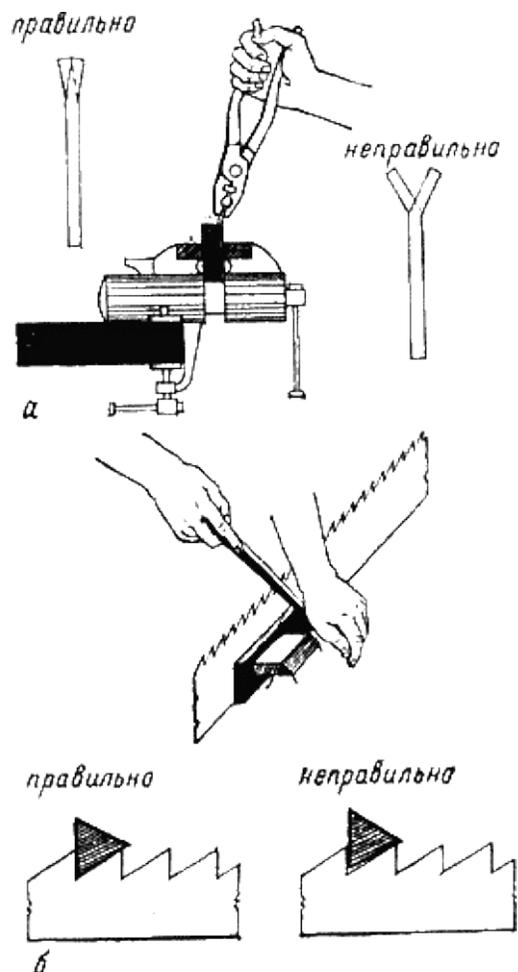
Подготовка пилы к работе: а — развод зубьев; б — заточка
